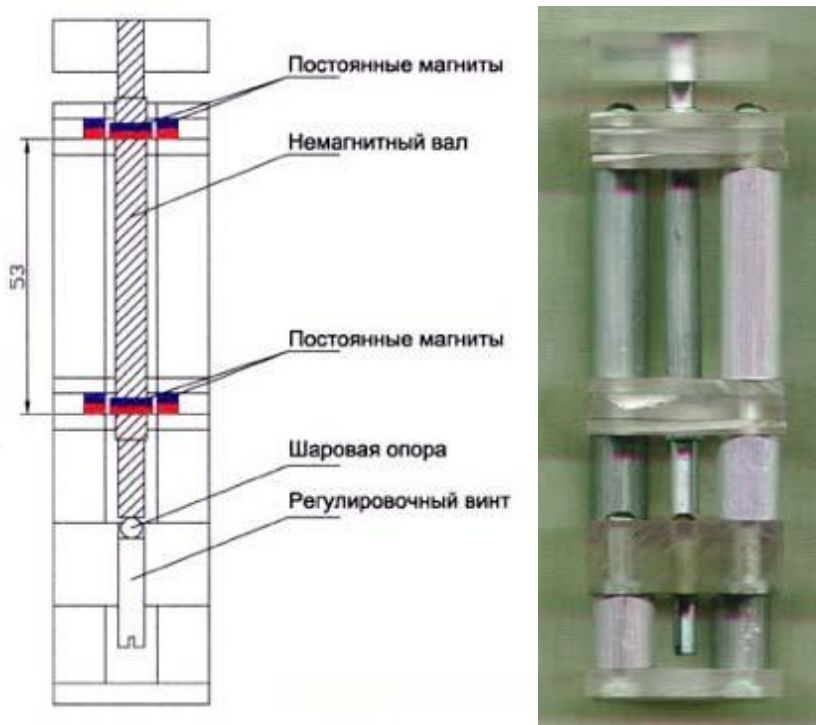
Макет устройства с двумя пассивными радиальными магнитными подшипниками.
